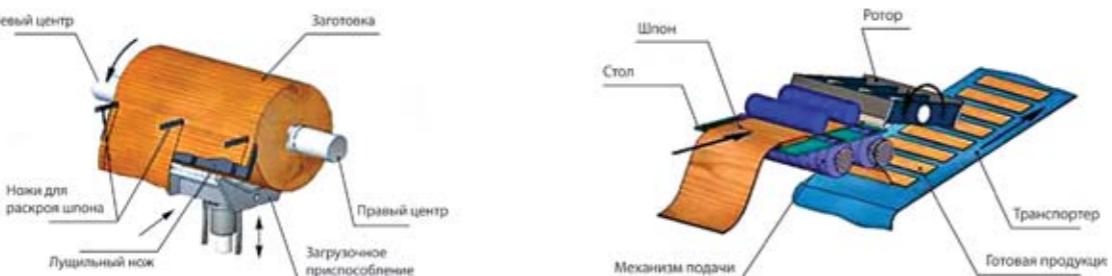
Лущильный станок и ножницы для рубки шпона на тарные дощечки (ГК «МАГР», г. Брянск)
